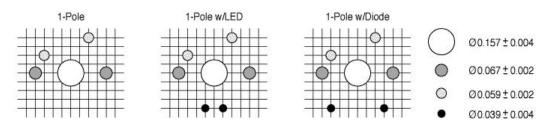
cherry MX 轴体-PCB 板焊接位置
